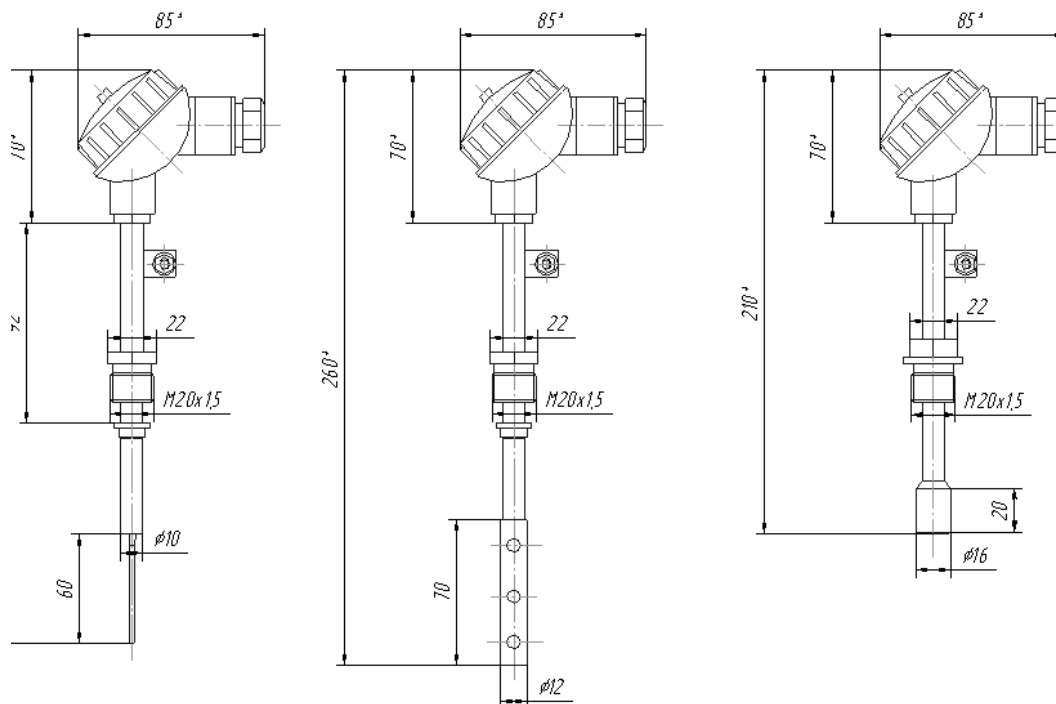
Внешний вид и габаритные размеры сигнализатора СЖУ-1-Э*:
